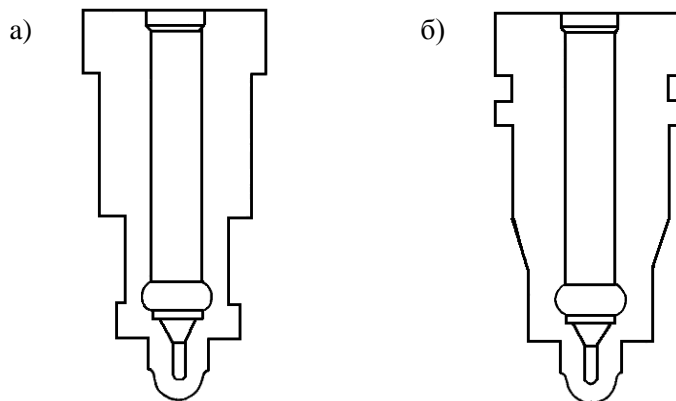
Конструкции распылителей без выточки (а) и с выточкой (б) двигателя ZD72/48
